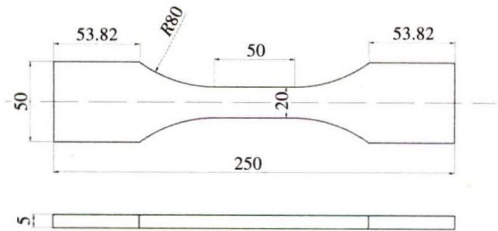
焊接接头疲劳试样形状及尺寸(mm)
